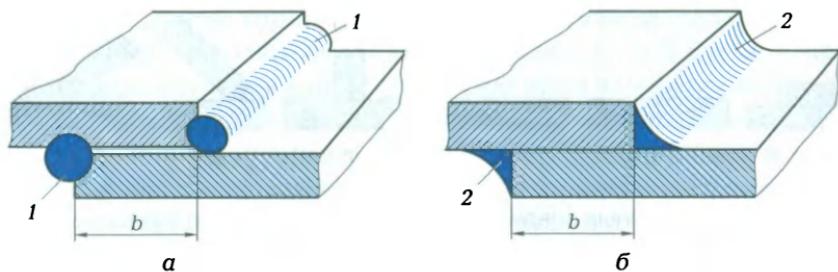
Форма и элементы сварного (а) и паяного (б) швов при соединении внахлестку:
